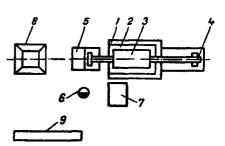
Схема планировки рабочего места изготовления оболочковых и цилиндрических стержней (крупносерийное производство):
